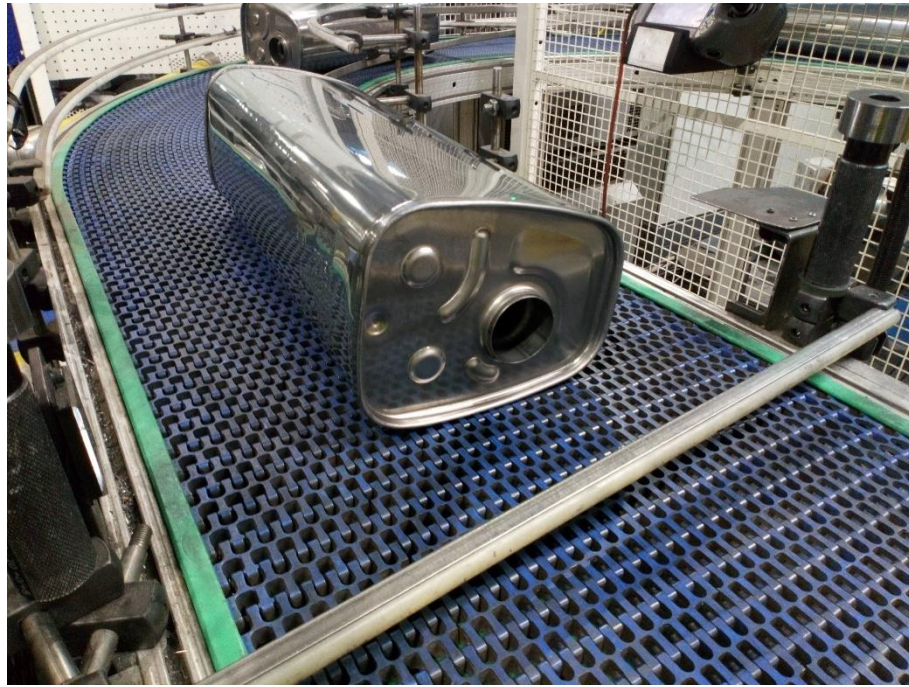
Vista frontal de caja y tapa colocadas, listas para ensamblaje
